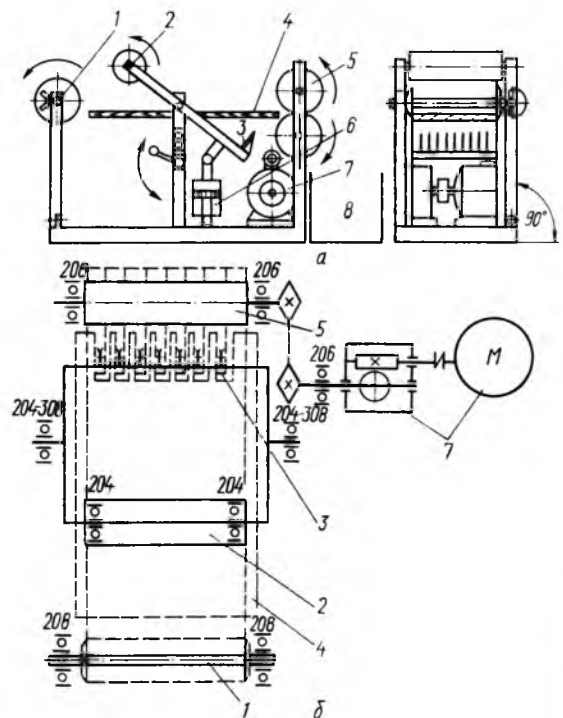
Схема станка для обрезки шлифовальной шкурки (а); кинематическая схема (б)
